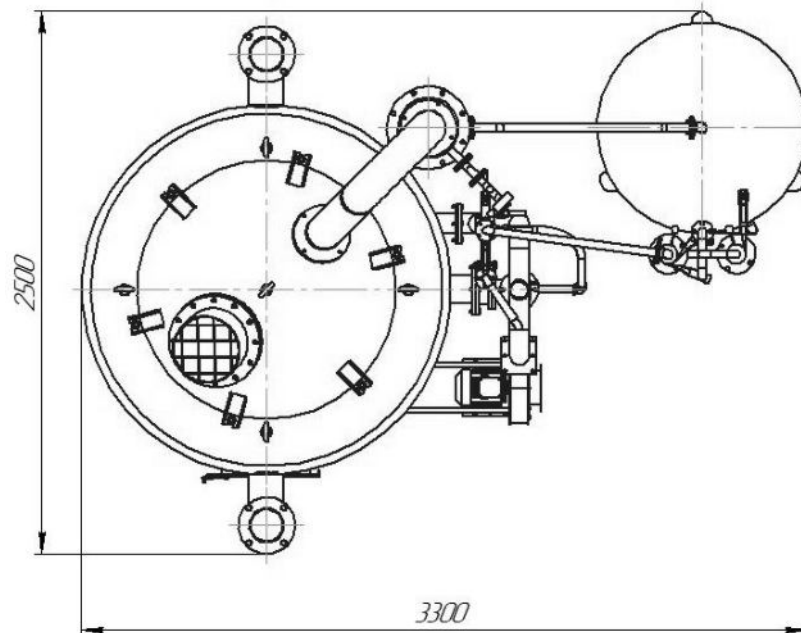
Общий вид пиролизной установки ФАРГОС-4М/FARGOS-4M (вид сверху)
